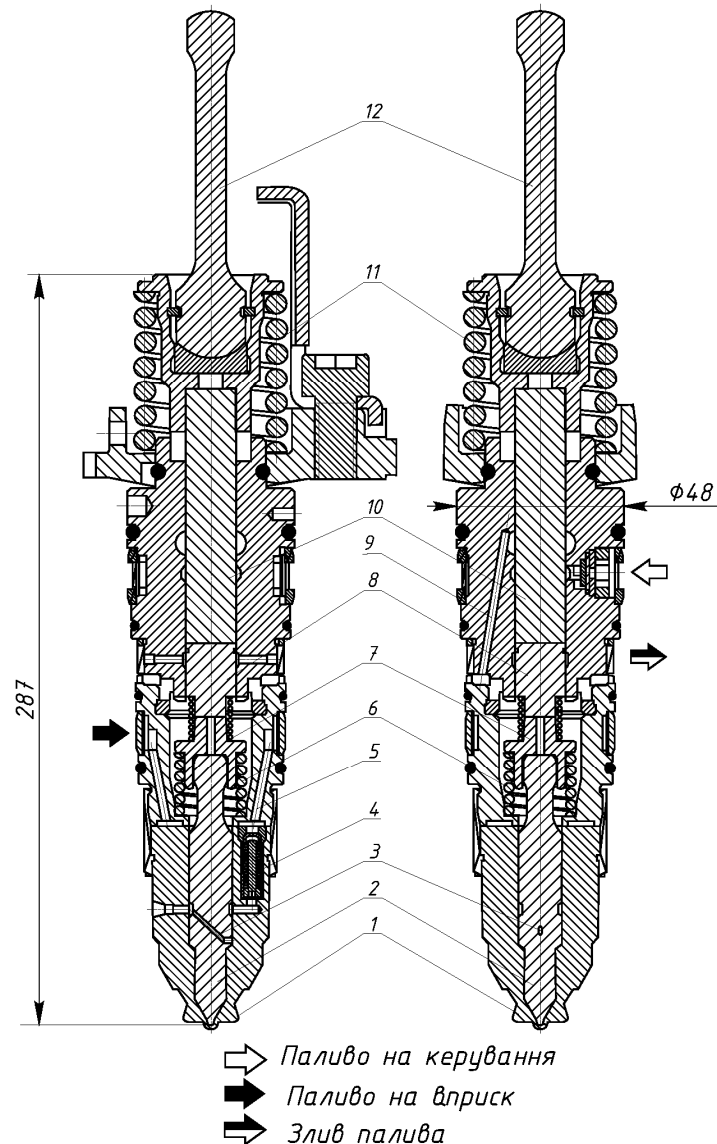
Насос-форсунка двигунів фірми Cummins з електронною системою керування подачею типу ISX. 1 – корпус розпилювача; 2 – нагнітальний плунжер; 3 – дренажний канал; 4 – наповнювальний клапан; 5 – наповнювальний канал; 6 – проміжна пружина; 7 – штовхач нагнітального плунжера; 8 – проміжний плунжер; 9 – канал відводу протічок; 10 – верхній плунжер; 11 – зворотна пружина; 12 – шток штовхача
